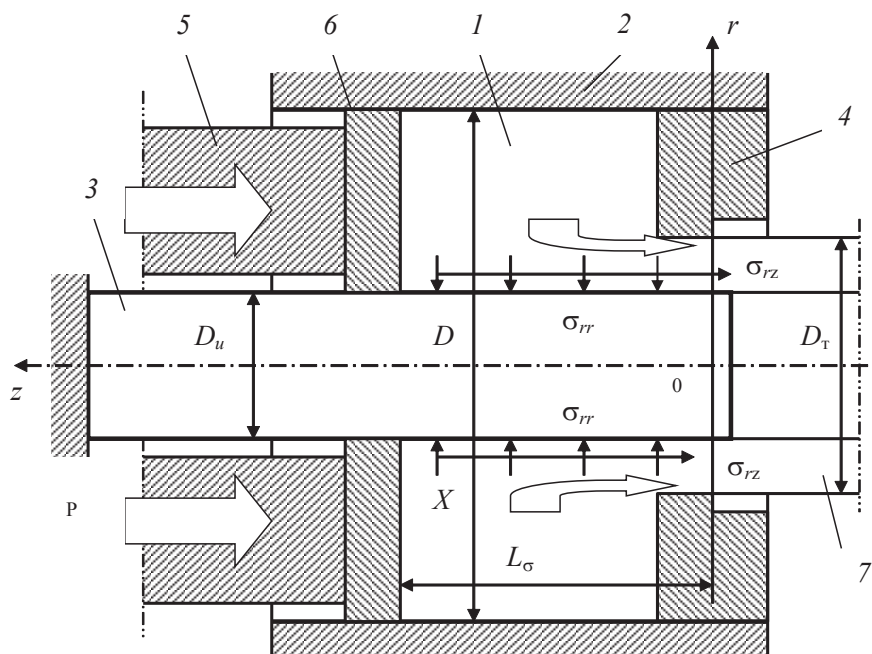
Расчетная схема нагружения иглы прессовой установки (обозначения в тексте)
